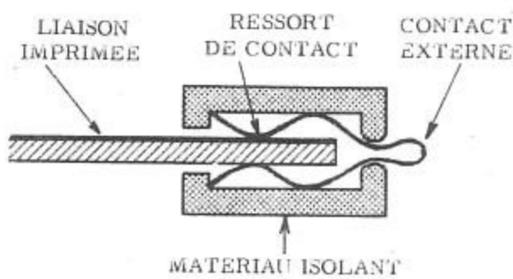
Coupe d'un contact à ressort, vu de côté.
